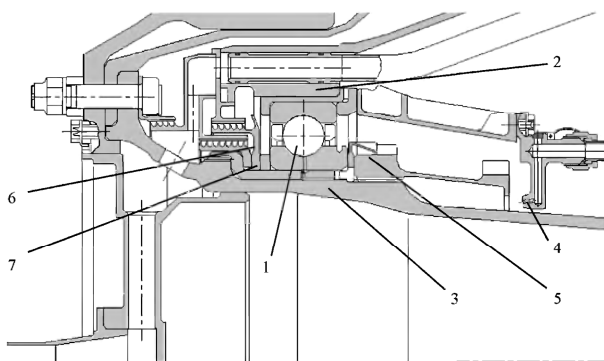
Опора шарикоподшипника ротора низкого давления (НД):
